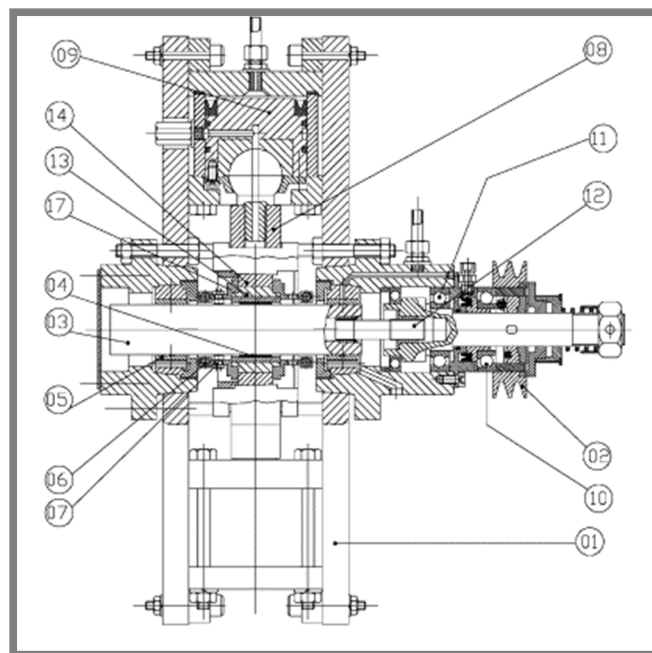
Stroj LP06, MIBA Bearing Group [3]
